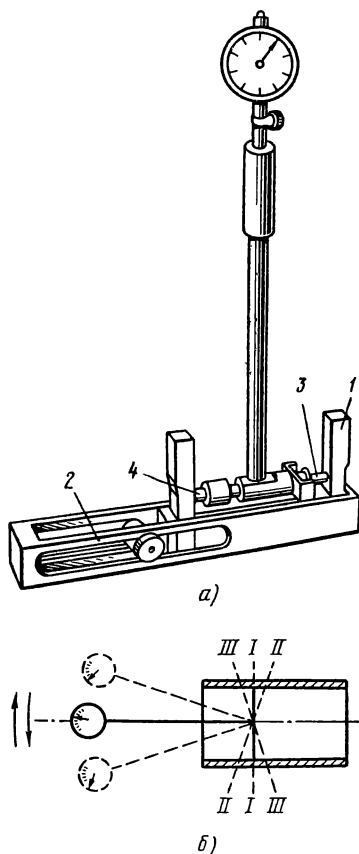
Установка нутромера на нуль (*a*), схема измерения (*б*)
